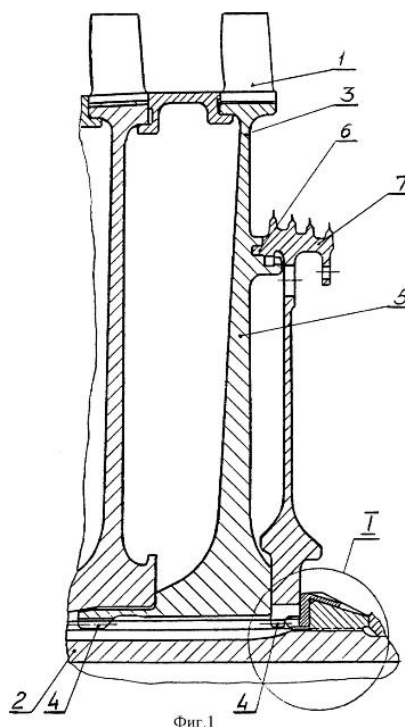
Продольный разрез ротора компрессора газотурбинного двигателя
